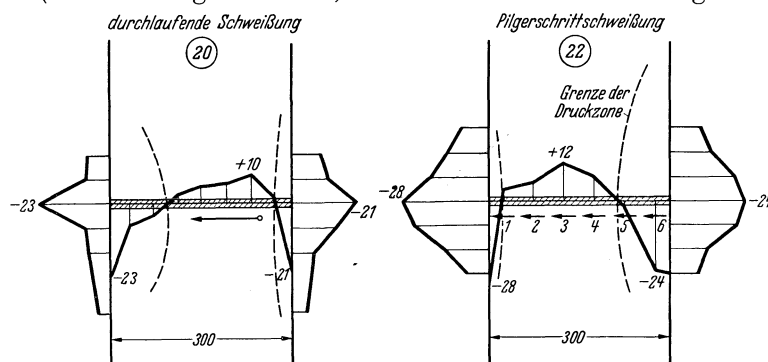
Schweißspannungen in stumpfgeschweißten Platten bei freier Schweißung.
